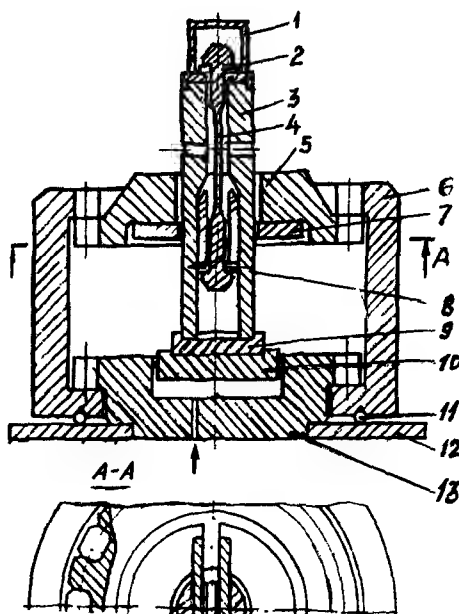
Установка для испытаний плоских толстолистовых сварных образцов при малоцикловом растяжении с максимальным усилием 1000 кН
